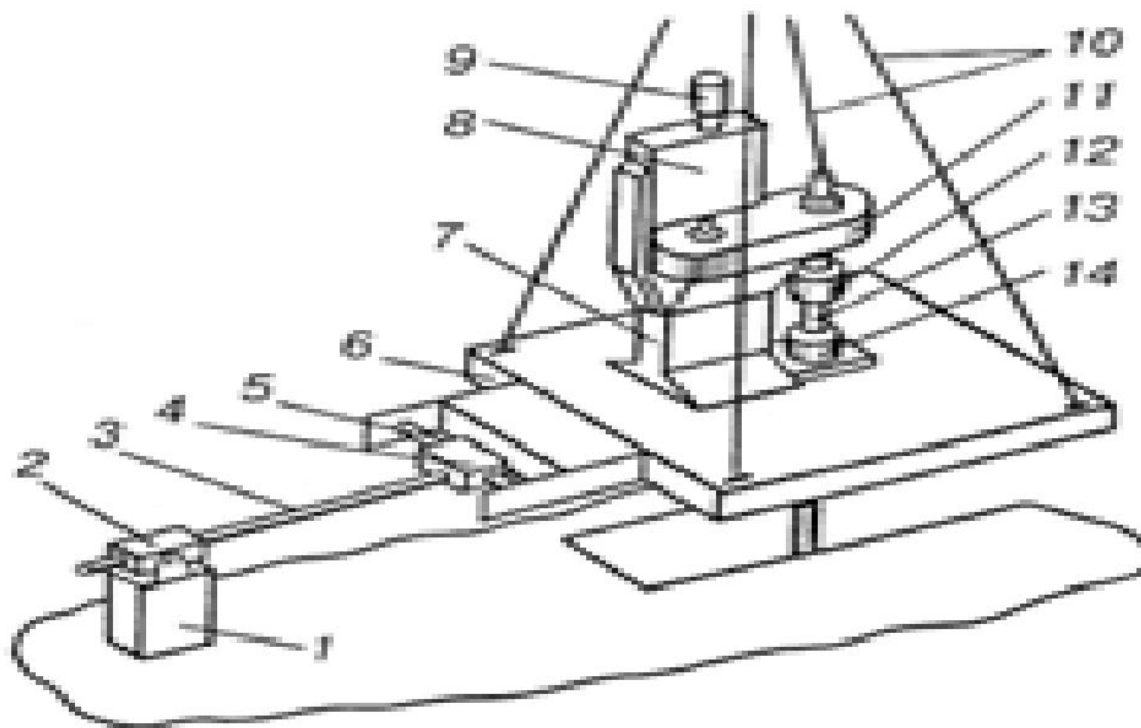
Буровой вращатель на колонне труб: 1 — стойка; 2 — каретка; 3 — продольная штанга; 4 — каретка; 5 — поперечная штанга; 6 — рабочая площадка; 7 — станина; 8 — коробка скоростей; 9 — гидромотор; 10 — тросы; 11 — редуктор; 12 — зажимный патрон; 13 — буровые трубы; 14 — патрон трубозаворота
